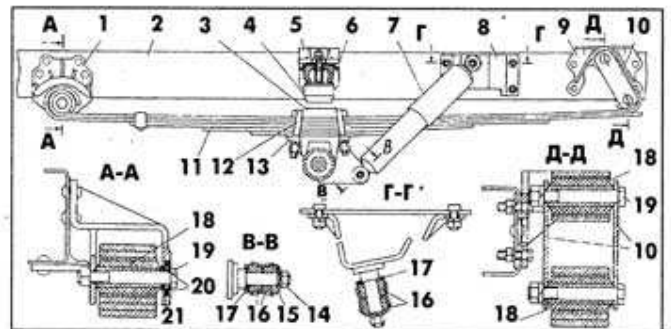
Передняя подвеска автомобилей типа 4x4: 1, 5, 8 и 9 – кронштейны; 2 – лонжерон рамы; 3 – наклад-ка; 4 – резиновая рессо-ра сжатия; 6 – чашка; 7 – амортизатор; 10 – серьга; 11 – рессора; 12 – стремянка; 13 – подушка рессоры; 14 – гайка; 15 – палец; 16 – резиновые втулки; 17, 20 и 21 – шайбы; 18 – резинометаллические шарниры; 19 – болт.
